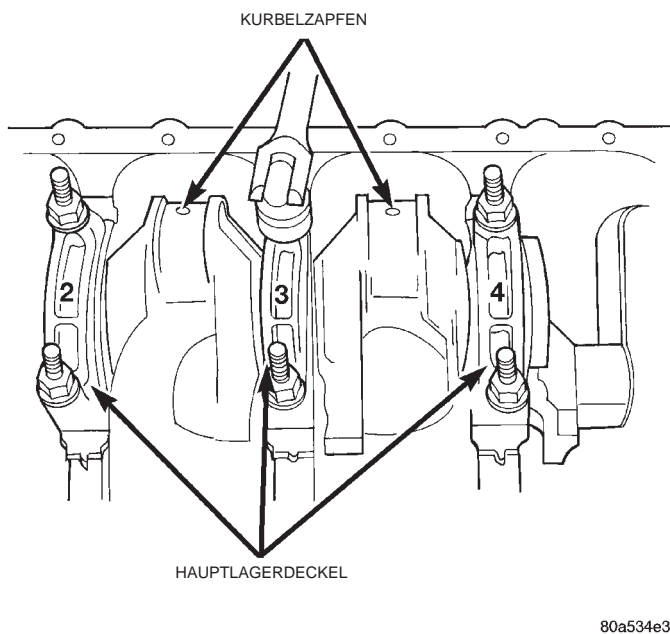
Ausbau/Hauptlagerdeckel und untere Lagerschalen
